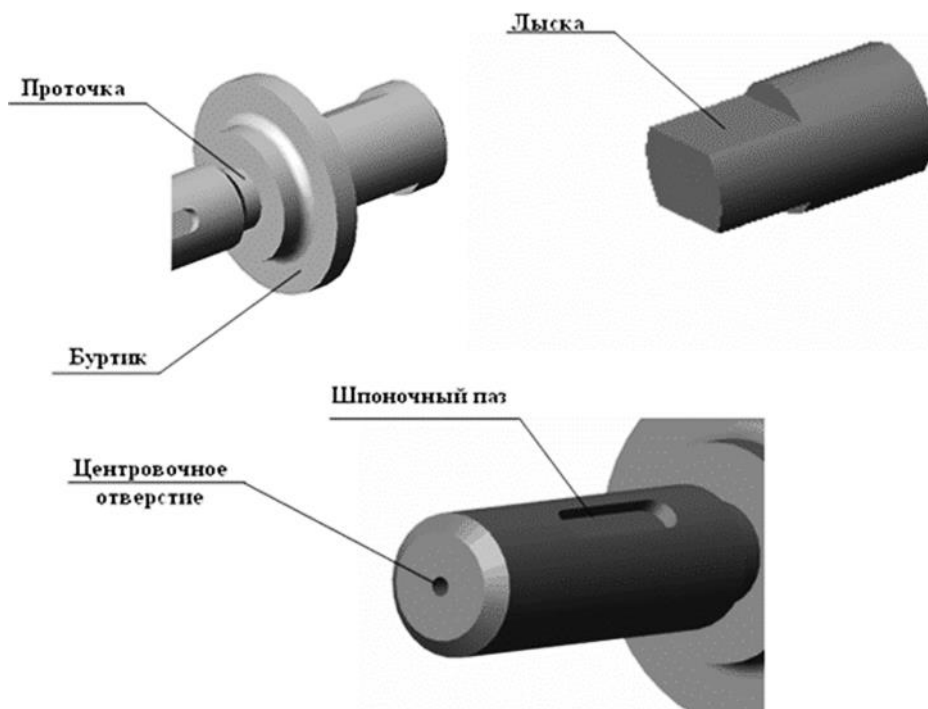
Образец выполнения конструктивных элементов корпусов.
